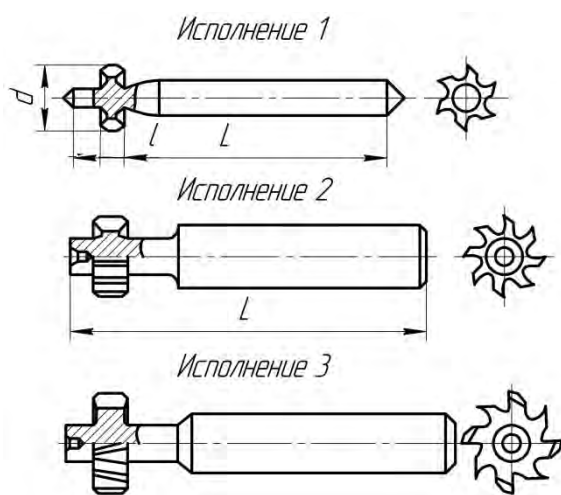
Фрезы для пазов сегментных шпонок
